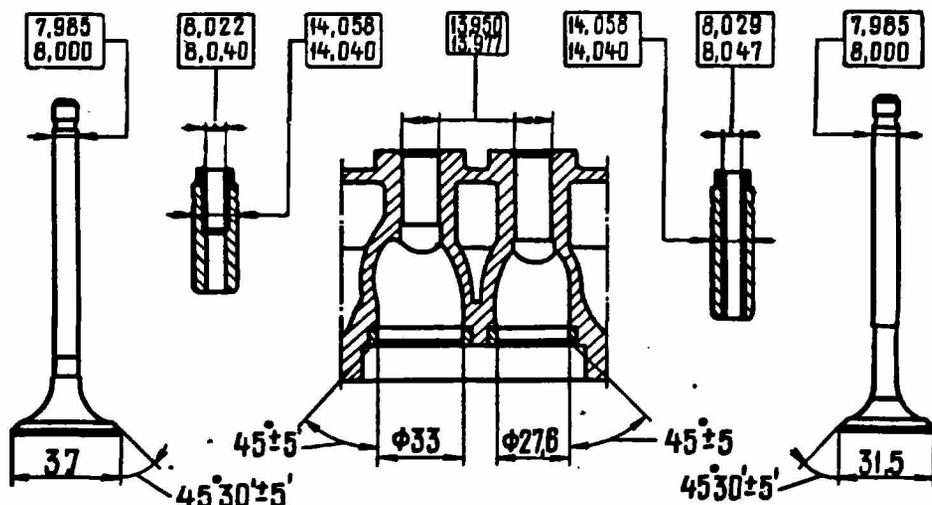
Основные размеры головки цилиндров, клапанов и направляющих втулок
